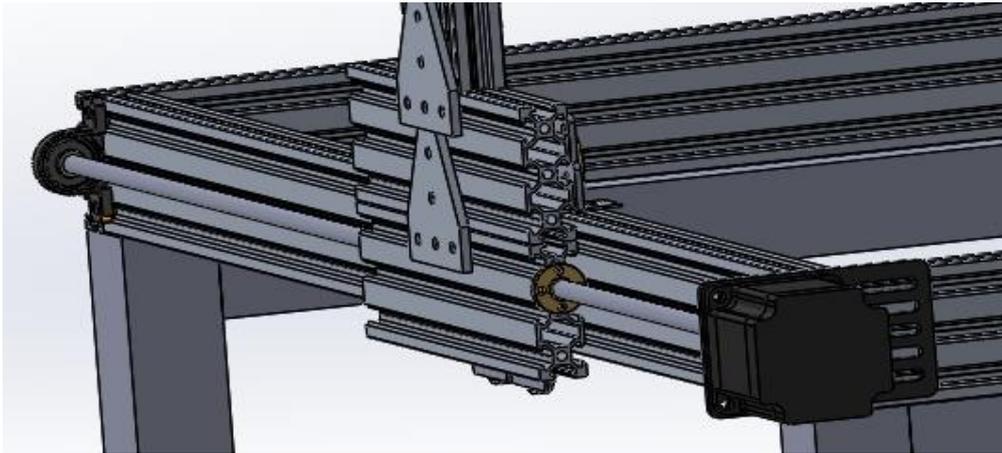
Assemblage complet de l'axe Y de la machine CNC 5
